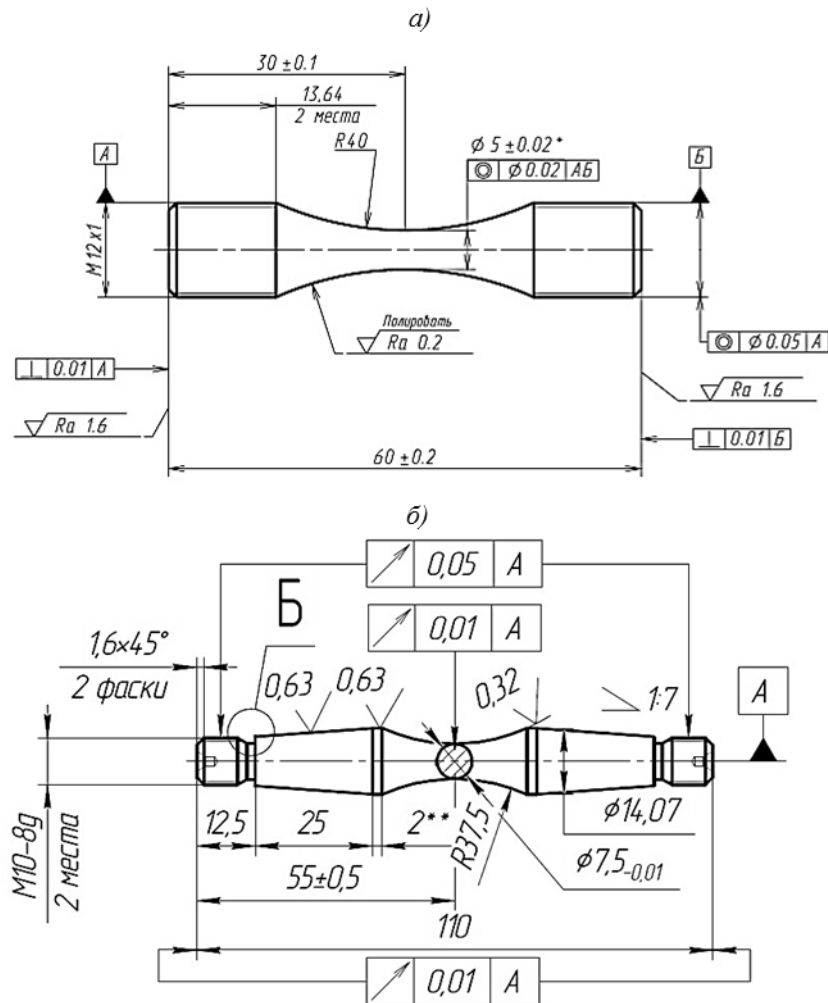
Гладкий цилиндрический образец с рабочей частью переменного сечения для испытаний по схемам нагружения «растяжение–сжатие» (а) и «чистый изгиб с вращением» (б)
